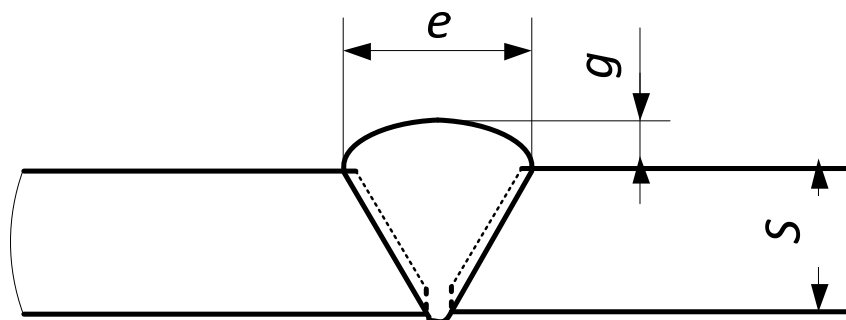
Эскиз объекта контроля (фрагмент сварного соединения)
